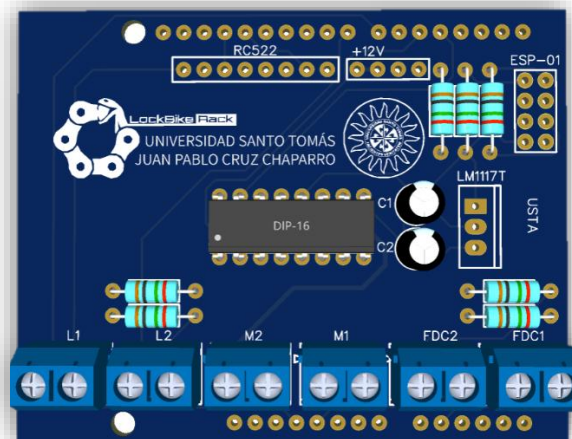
Diseño final PCB, Proteus 8 Profesional - LockBikeRack
